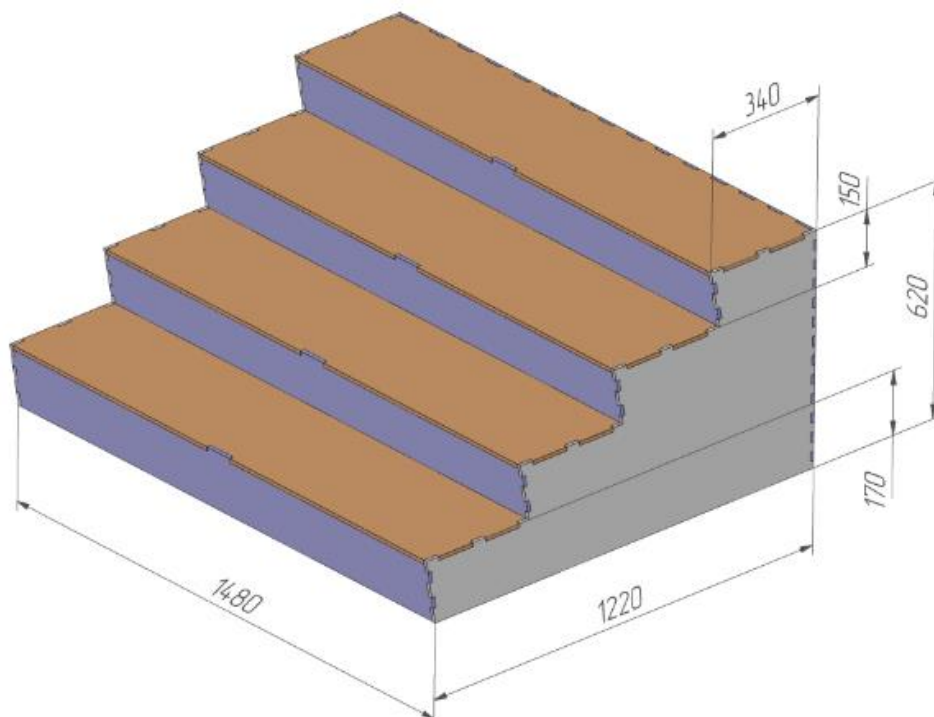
Лестничный марш (габаритные размеры)
